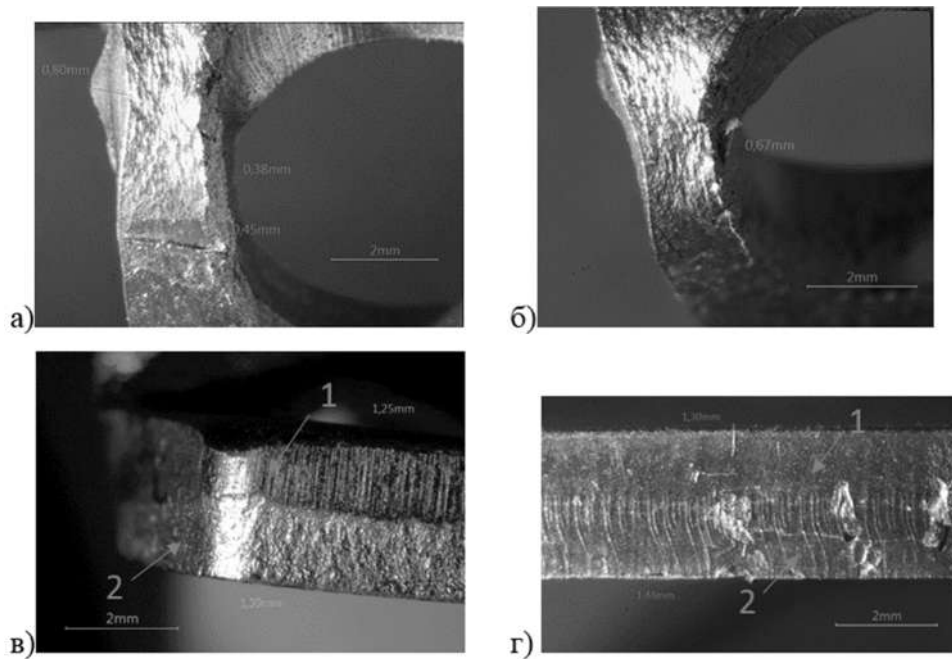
Боковая поверхность листа кронштейна, полученного из заготовки после лазерной резки:
